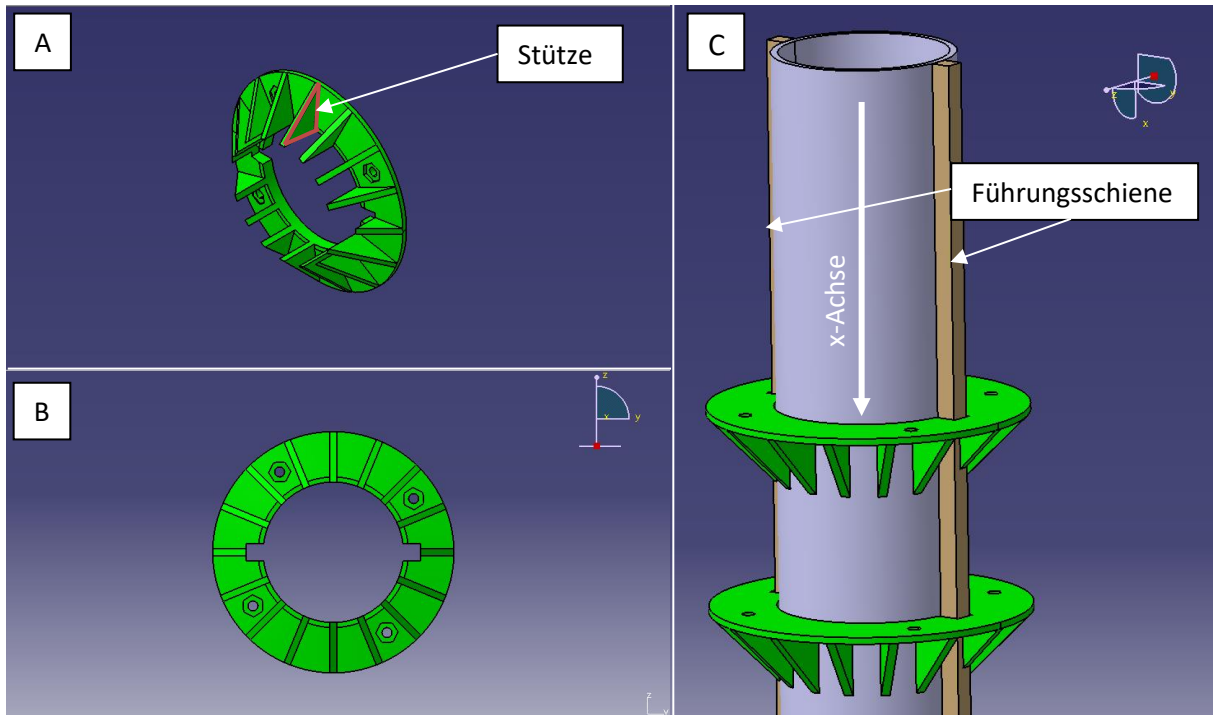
Bild A: Isometrische Darstellung des hinteren Winkels; Bild B: Draufsicht von unten auf den hinteren Winkel; Bild C: Winkel für den hinteren Hauptspanträger und die Positionierungsplatte der Hauptverbinder.
